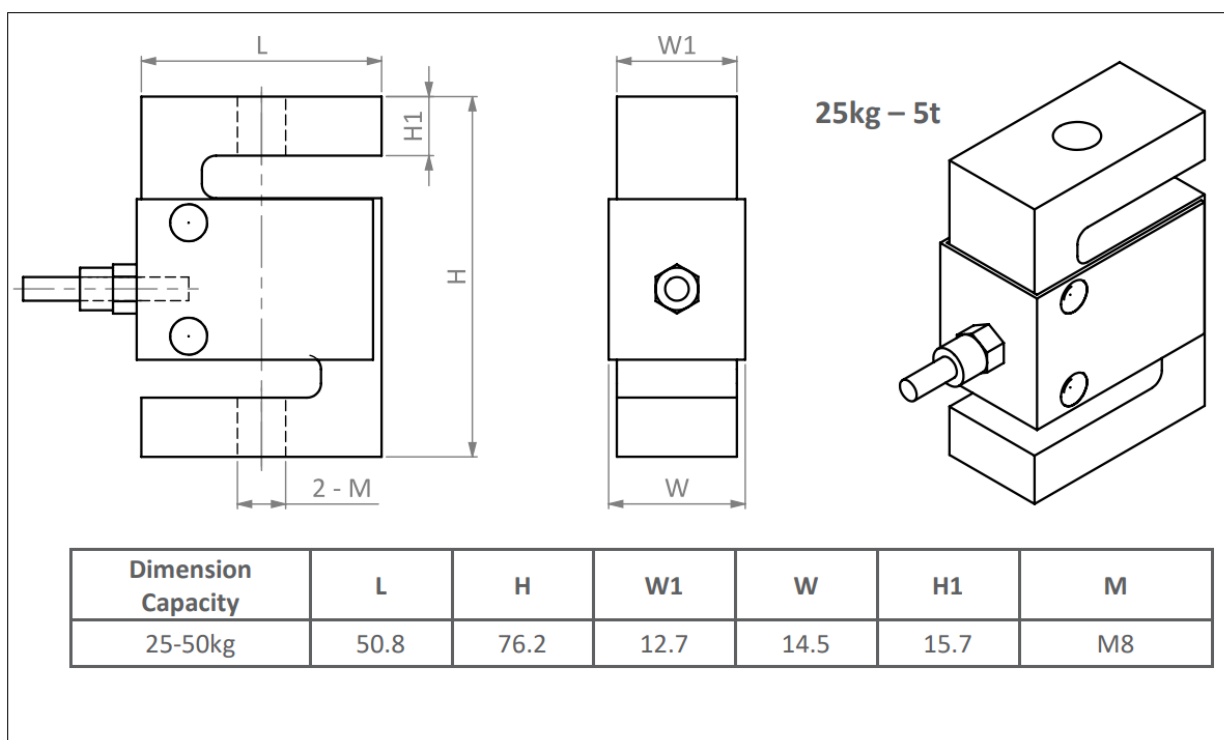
Габаритні розміри датчика H3-C3-50kg-3B
